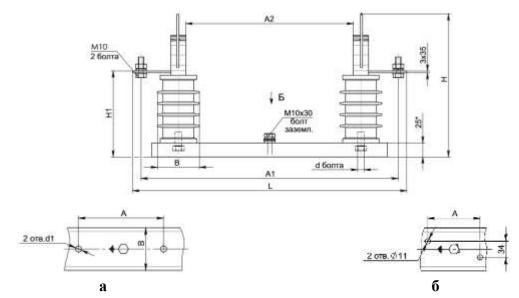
Габаритные, присоединительные и установочные размеры основания.
